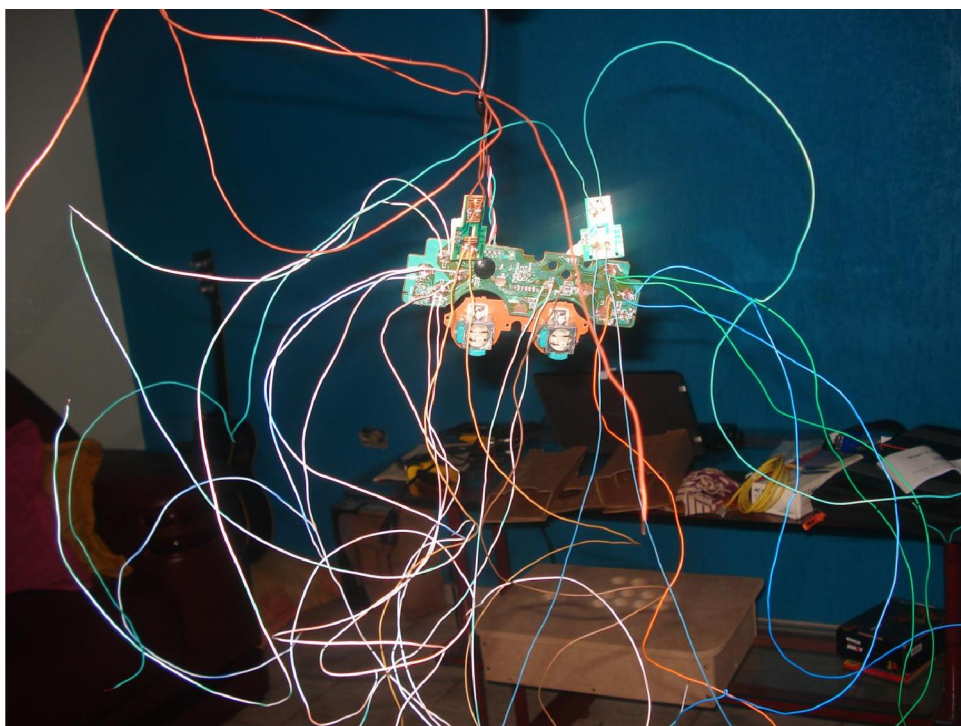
Placa de Controle USB com os fios de cobre soldados
